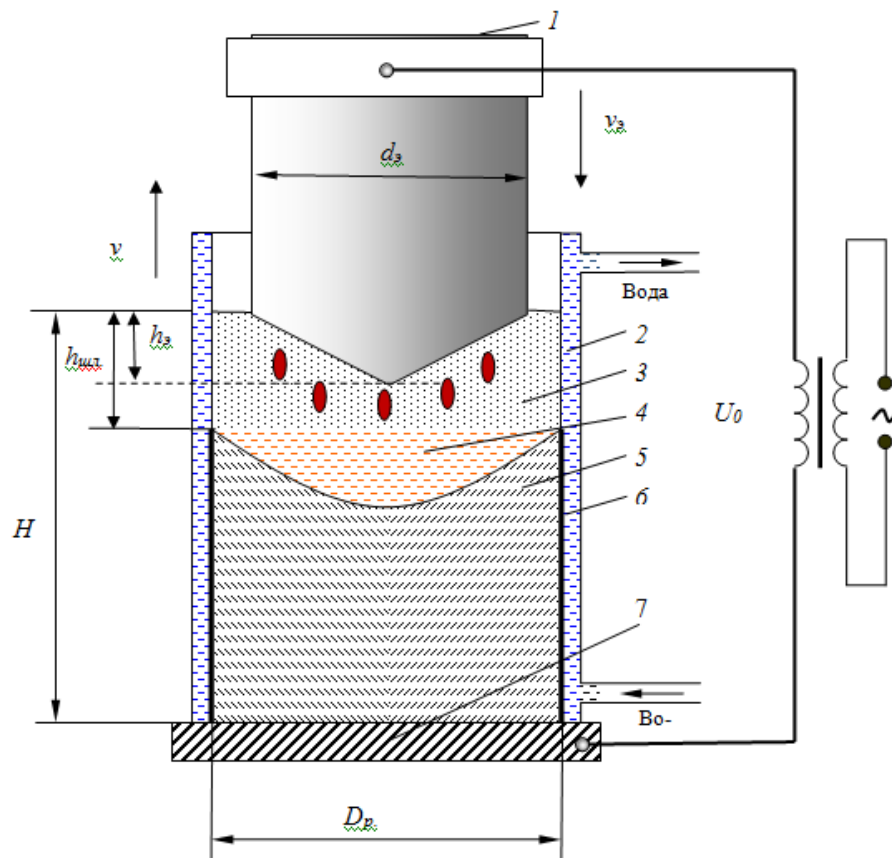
Схема установки электрошлакового переплава: 1 – электрод; 2 – кристаллизатор; 3 – расплавленный шлак; 4 – ванна жидкого металла; 5 – слиток; 6 – корочка твердого шлака; 7 – поддон
